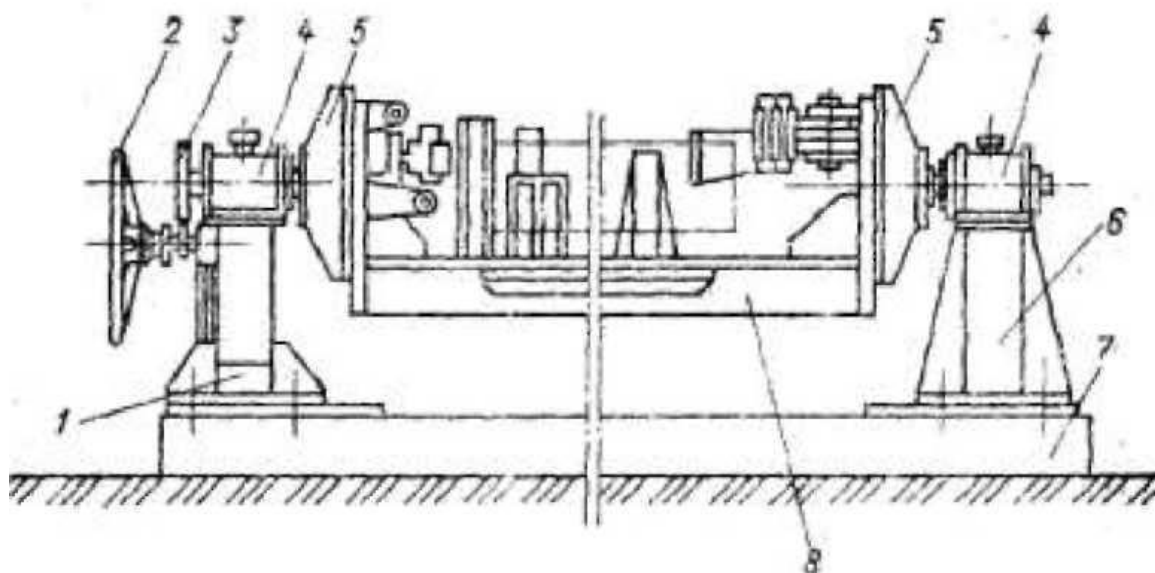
Кондуктор-кантователь для сборки элементов
